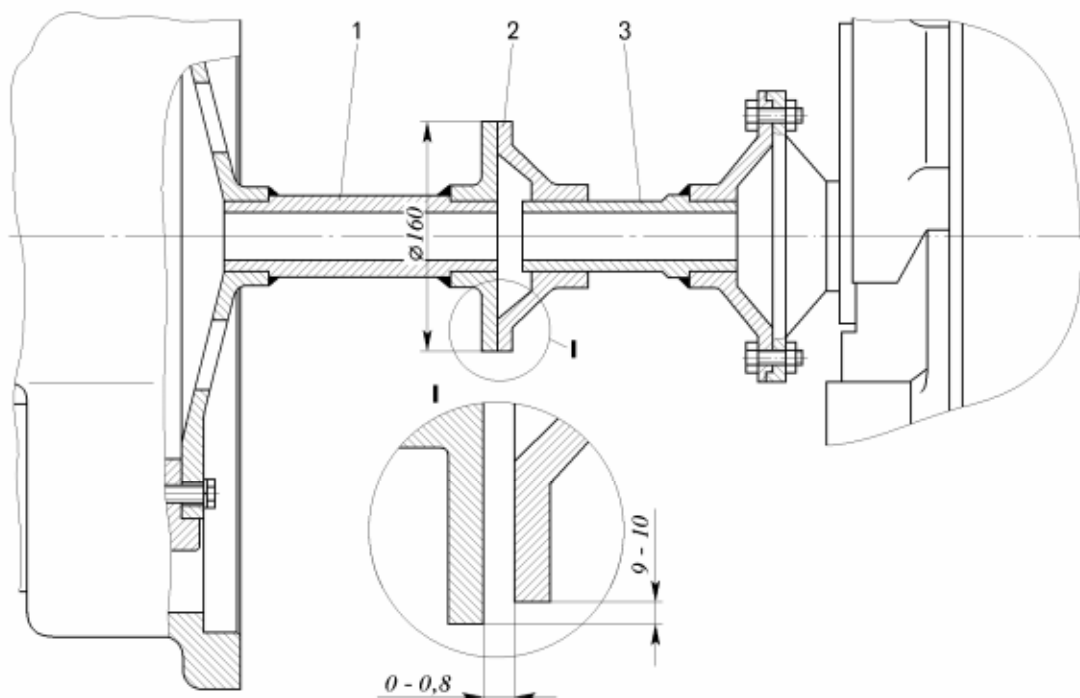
Приспособление для проверки соосности и параллельности осей ведущего вала гидромеханической передачи и коленчатого вала двигателя:
